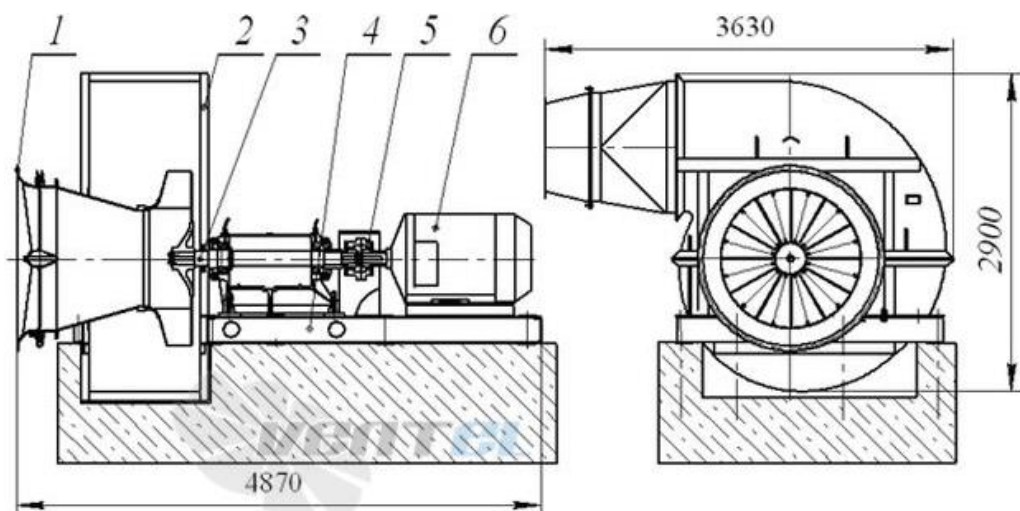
Схема вентилятора ВЦП-16М: 1- направляющий аппарат; 2- корпус; 3-ротор; 4- рама; 5- муфта; 6- электродвигун.
